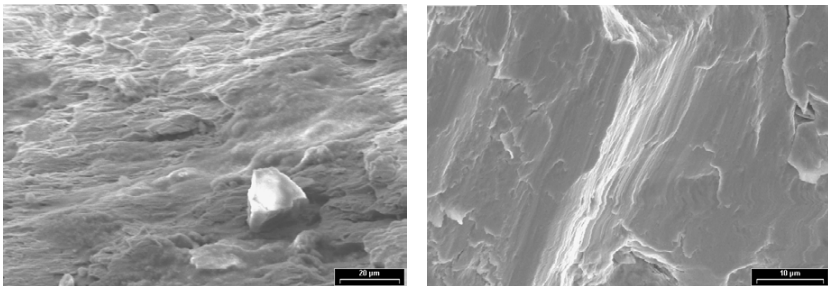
/6: Scheinbare Schwingbruchmerkmale im Bereich einer mechanisch bearbeiteten Oberfläche; Tatsächlicher Schwingbruch am gleichen Bauteil
